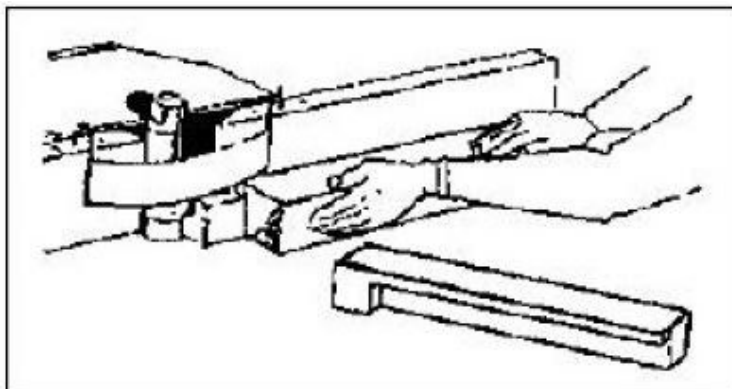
Fräsen von Werkstücken mit kleinem Querschnitt
